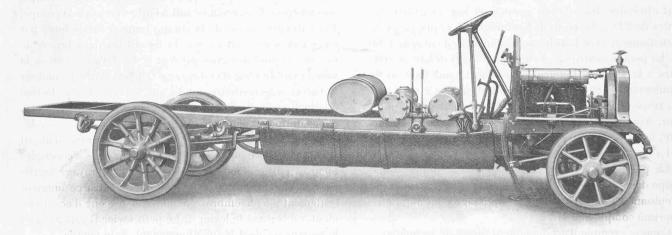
Châssis d'une pompe automobile à incendie Adler.
